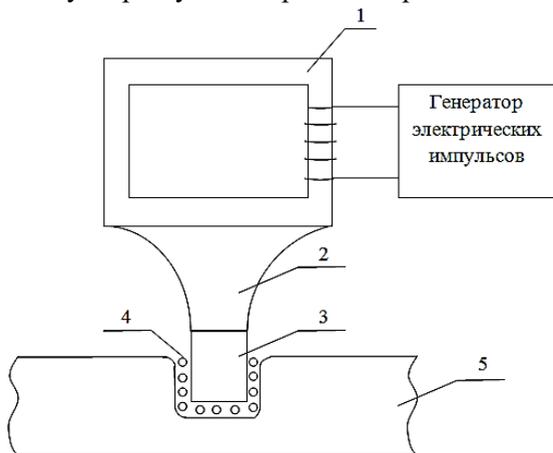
Схема ультразвукового резания: 1 – ультразвуковой преобразователь (магнитостриктор); 2 – концентратор ультразвуковых колебаний; 3 – инструмент; 4 – суспензия на основе абразивных частиц; 5 – обрабатываемая деталь
